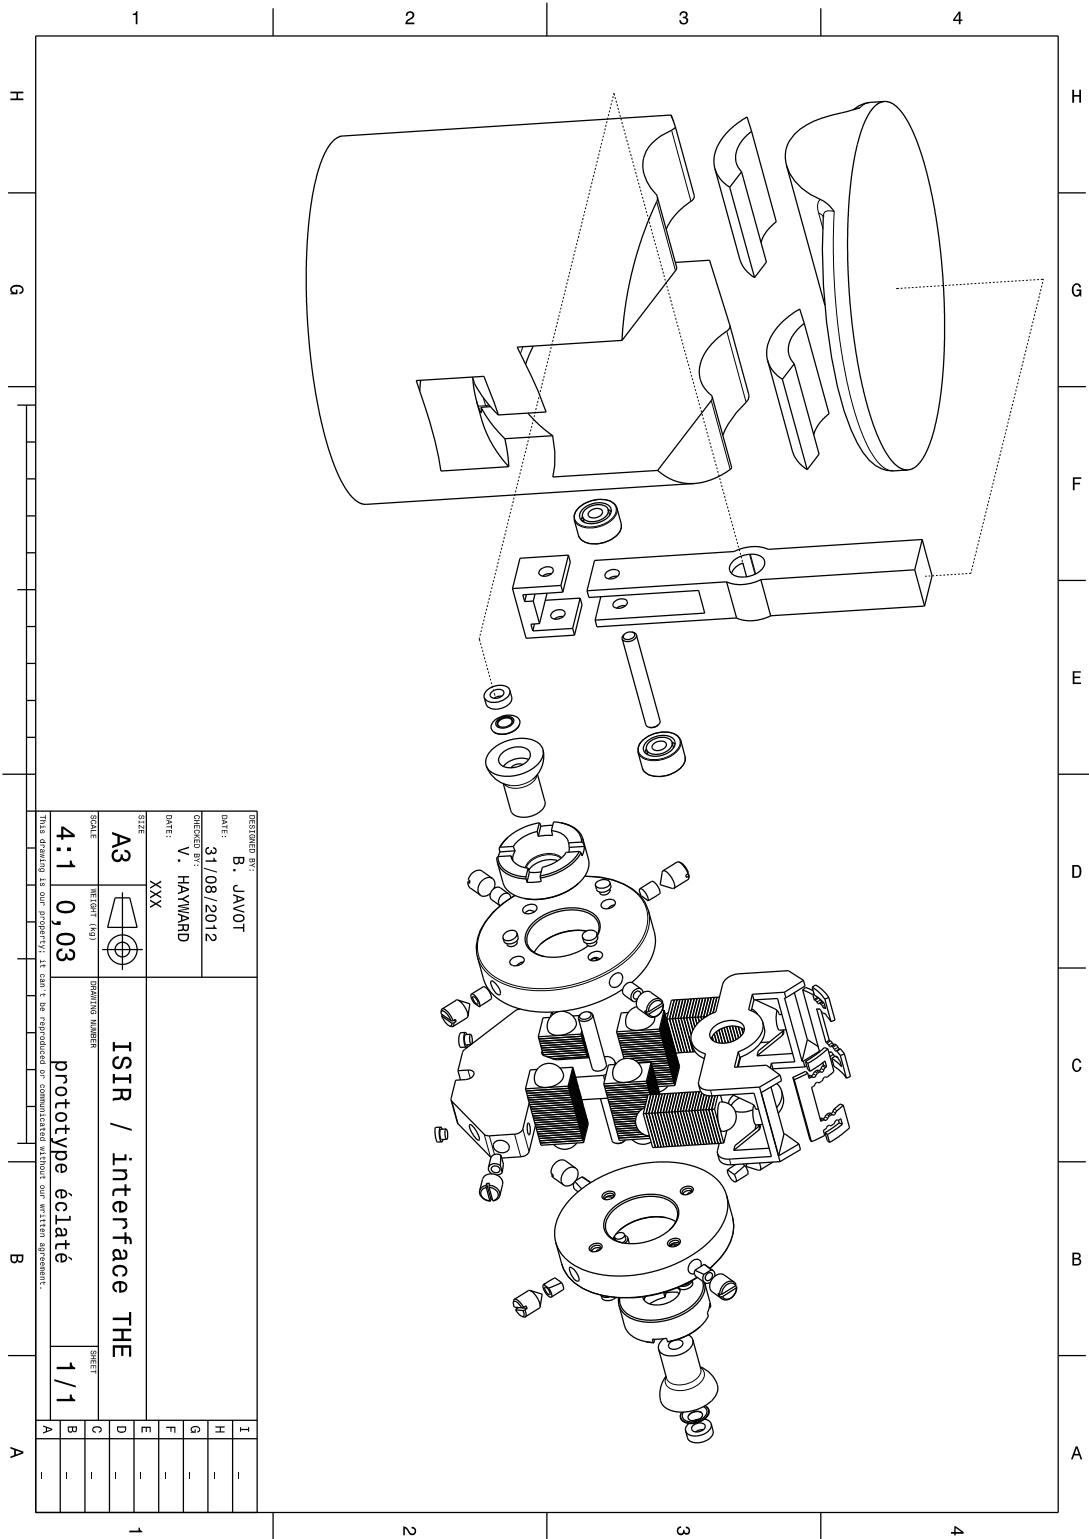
Éclaté moteur miniature : pign 1 mm et étrier 22 mm de diamètre.
